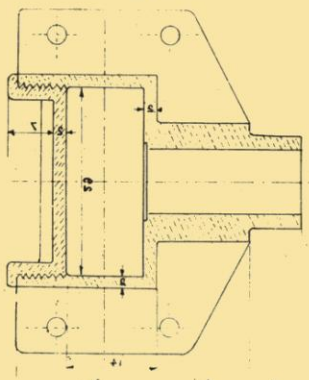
Sezione del carter secondo un piano mediano orizzontale
